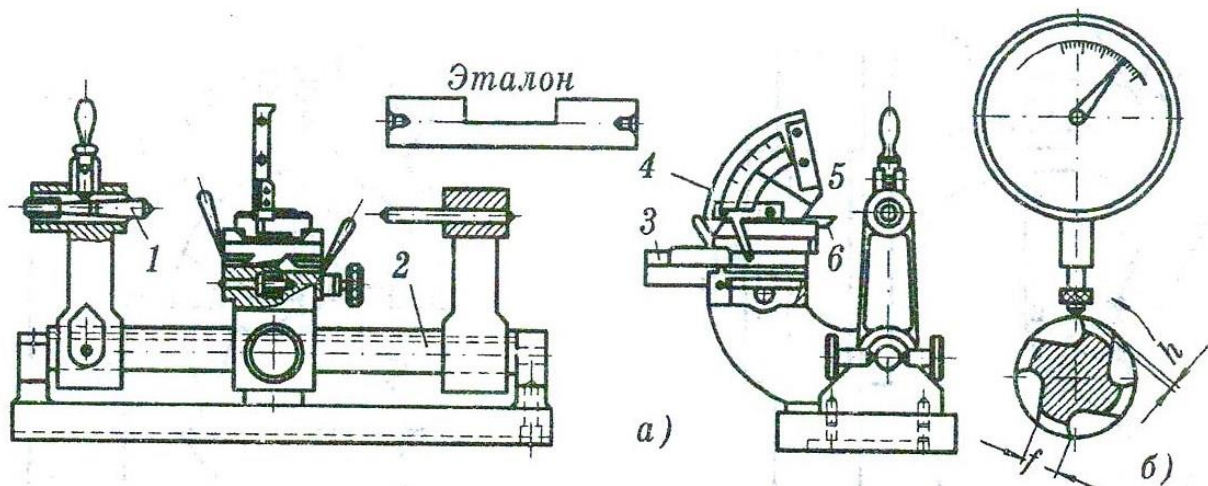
Прибор для измерения переднего угла метчиков: б - измерение величины затылования с помощью индикатора; 1 - центры; 2 - ось; 3 - каретка; 4 - измерительное устройство; 5 - стрелка; 6 - колодка
